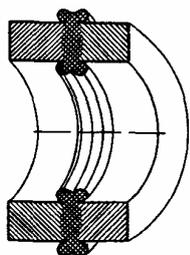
Соединение, выполненное сваркой нагретым инструментом
